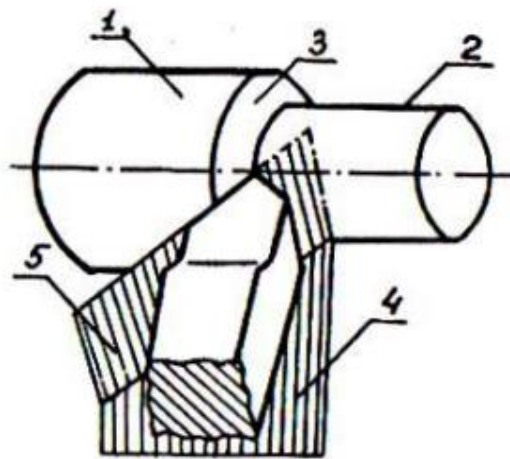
Поверхні та площини при токарній обробці: 1 – поверхня, що обробляється, з якої зрізають шар матеріалу (припуск); 2 – оброблена поверхня, що виходить після зрізання шару матеріалу; 3 – поверхня різання, утворюється головною ріжучою кромкою різця; 4 – основна площина, паралельна напрямкам поздовжньої та поперечної подачі; 5 – площина різання, проходить через головну ріжучу кромку щодо поверхні різання заготовки. Головні кути вимірюються в перерізі головної січної площини А-А, яка перпендикулярна до проекції головної ріжучої кромки на основну площину. γ – головний передній кут – кут між передньою поверхнею та площиною, перпендикулярною до площини різання.
